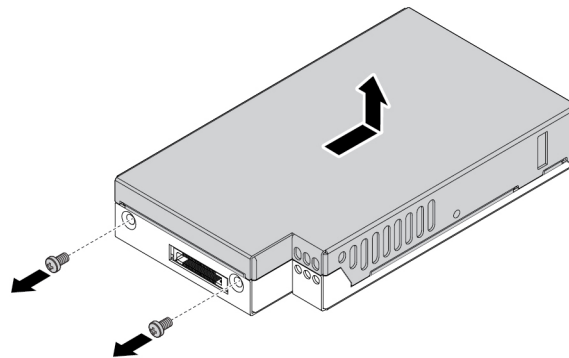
Removendo a tampa do suporte da unidade de estado sólido M.2
